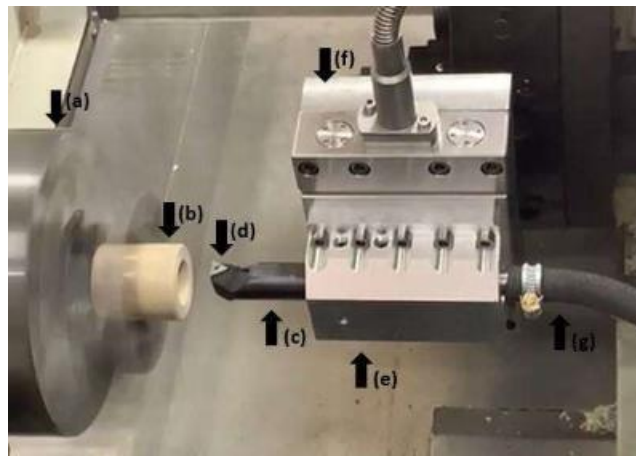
Setup experimental com (a) placa de fixação do corpo de prova, (b) corpo de prova, (c) barra de mandrilar, (d) ferramenta de torneamento, (e) bucha e suporte de fixação, (f) dinamômetro e (g) ar comprimido.
